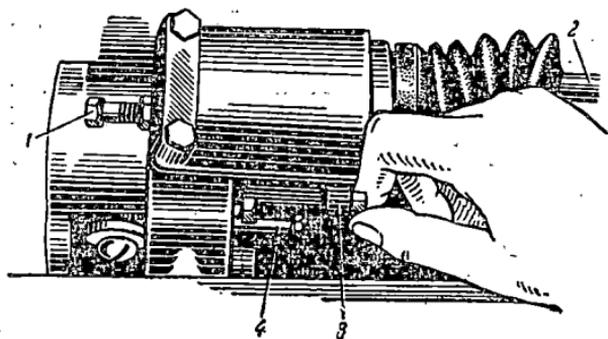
Проверка свободного хода рычага ручного привода тормозов прицепа на тракторе К-700:
